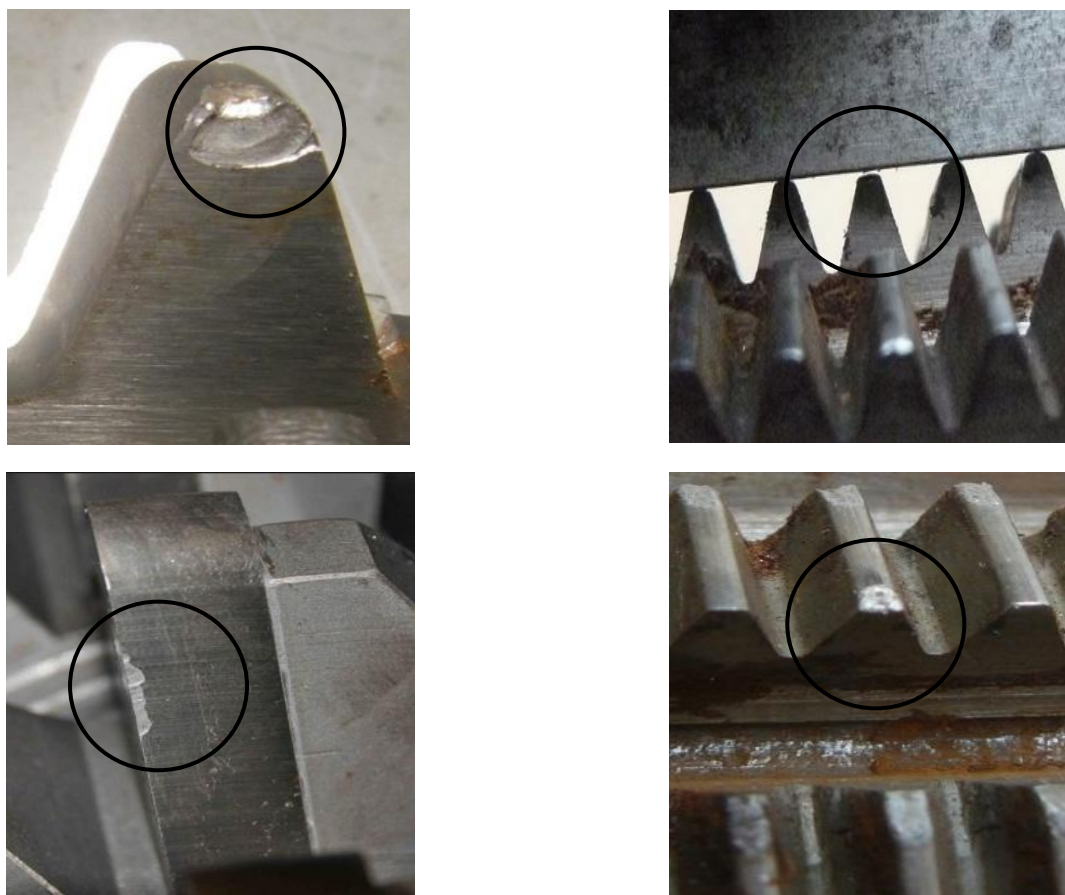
Разрушение и износ зубьев червячных фрез $m=14$ в процессе обработки
